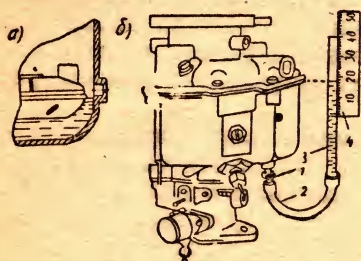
Проверка уровня топлива в поплавковой камере карбюратора:
